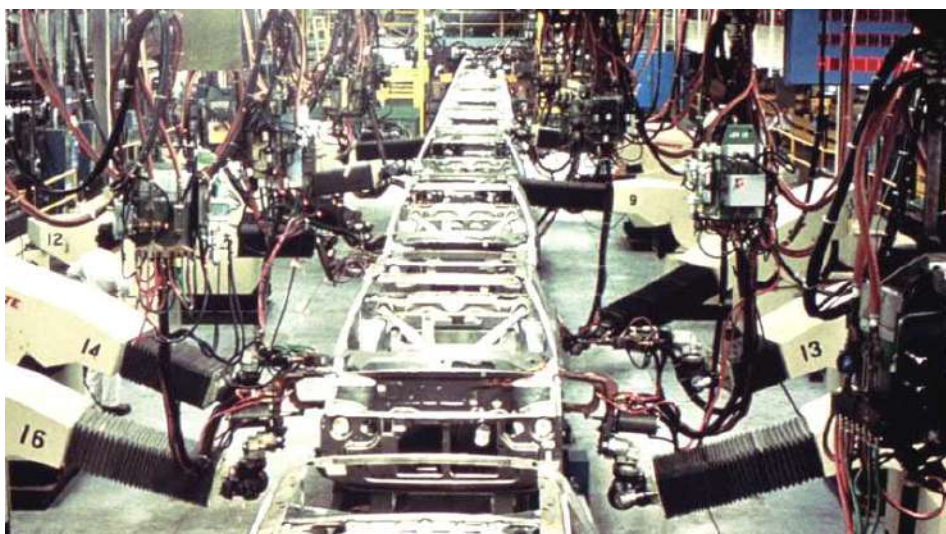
Роботы Unimate на линии точечной сварки.
